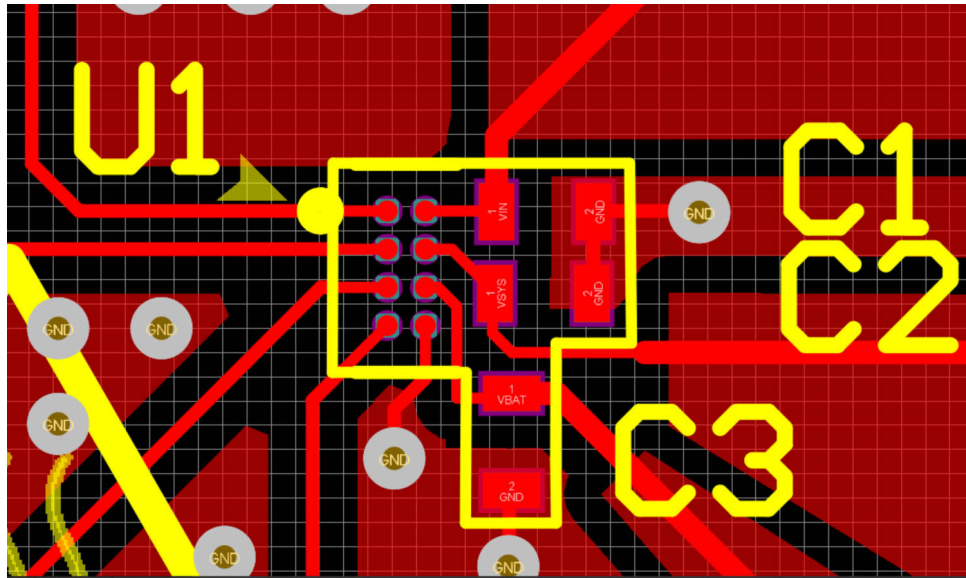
BQ25180 扇出，焊盘上走线为 5mil 至 6mil
